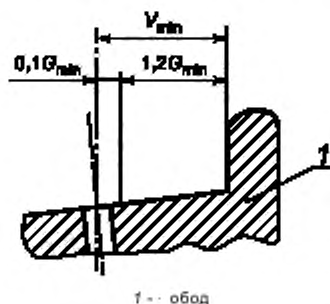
Расположение отверстия для вентиля камерной шины
